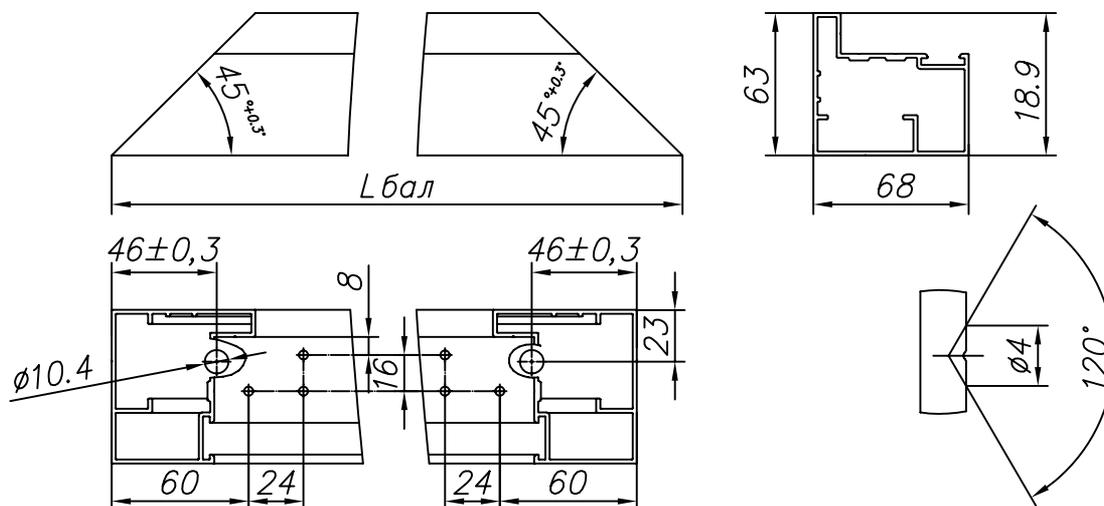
Изготовление верхней балки (ворота без перекладины)
